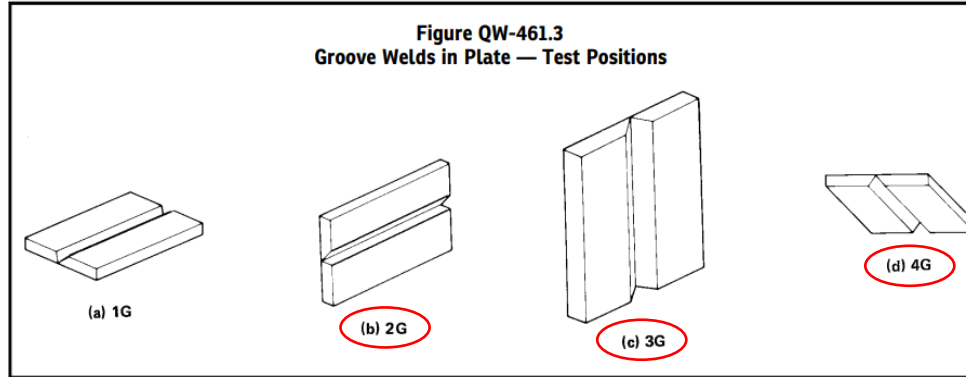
Posição de Soldagem Qualificação de Soldadores – Fonte: ASME Sec. IX – Ed.2015
